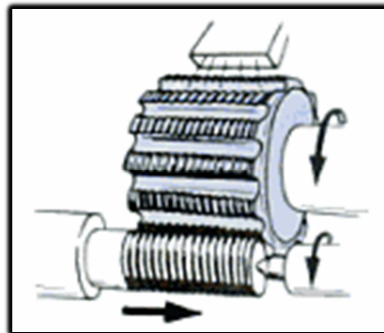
Máquina Fresadora de roscas<sup>18</sup>
